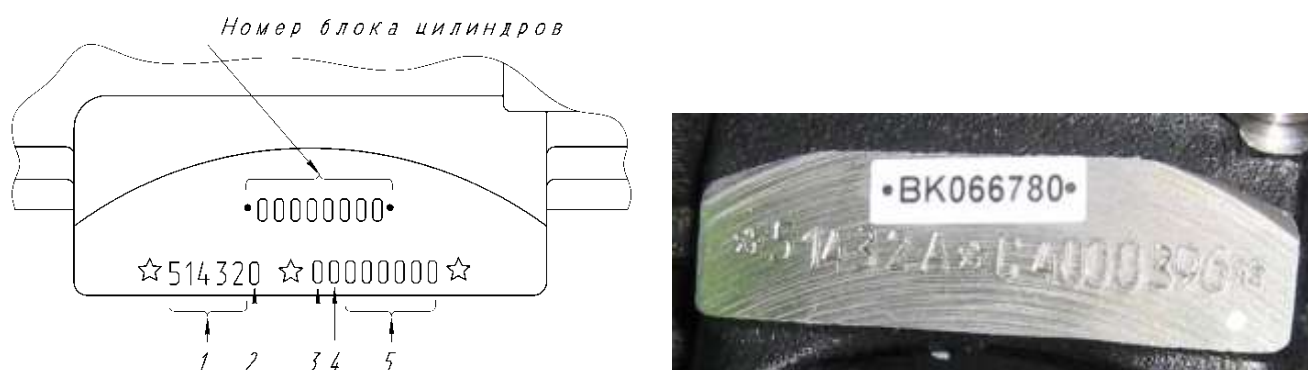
Маркировка двигателя ударным способом на блоке цилиндров:
